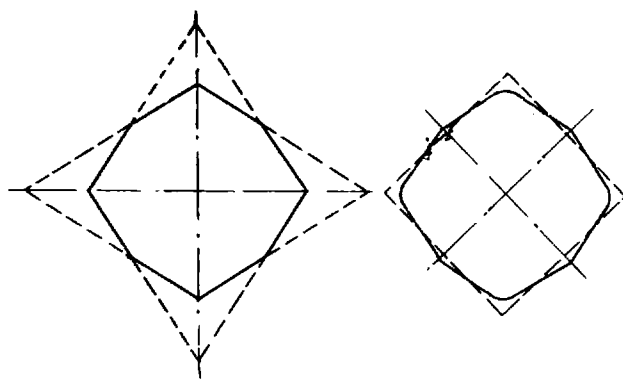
Схема получения квадратной заготовки при прокатке в ромбических калибрах
